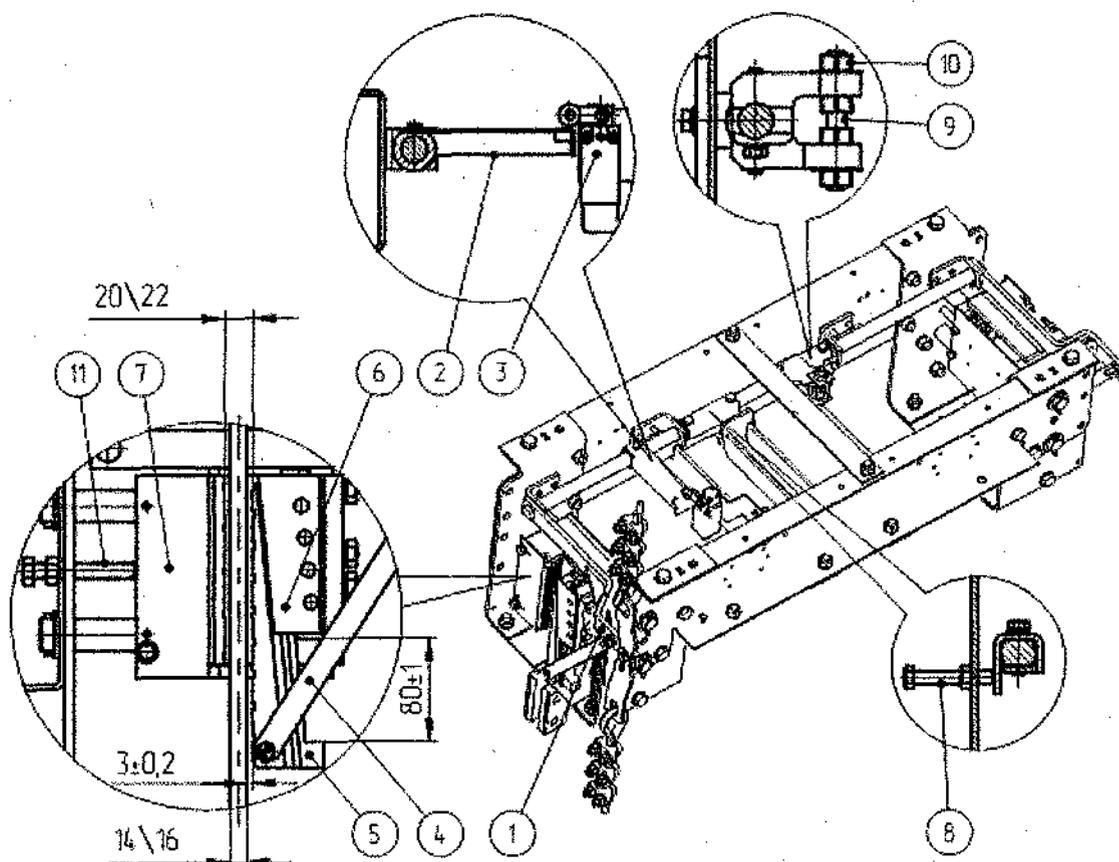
Ловитель одностороннего действия: 1 - Рычаг троса; 2 - планка; 3 - выключатель; 4 - троса; 5 - клин; 6 - колодка; 7 - колодка тормозная; 8 - болт регулировочный; 9 - шпилька; 10 - гайка; 11 - болт регулировочный.
